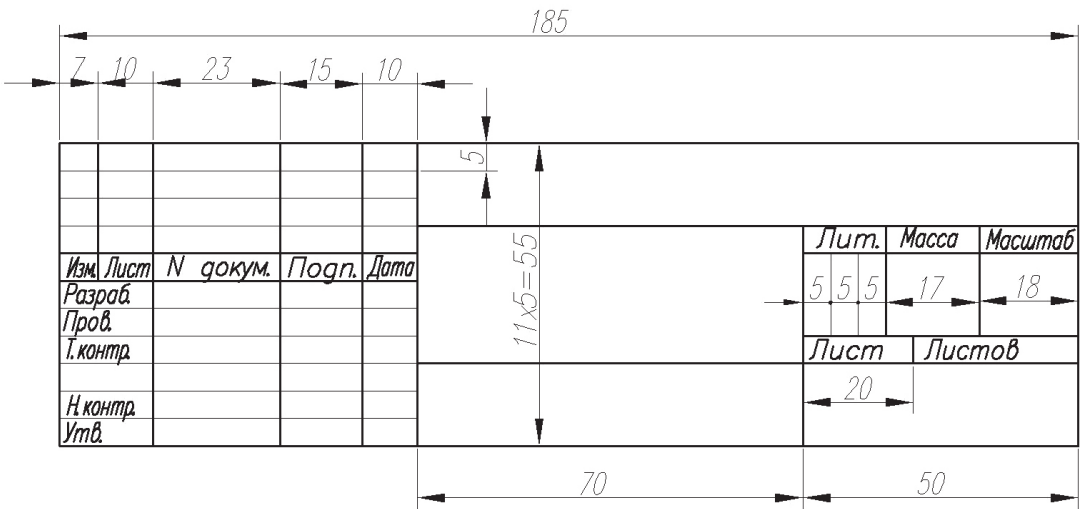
Основная надпись для чертежей и схем — форма 1
